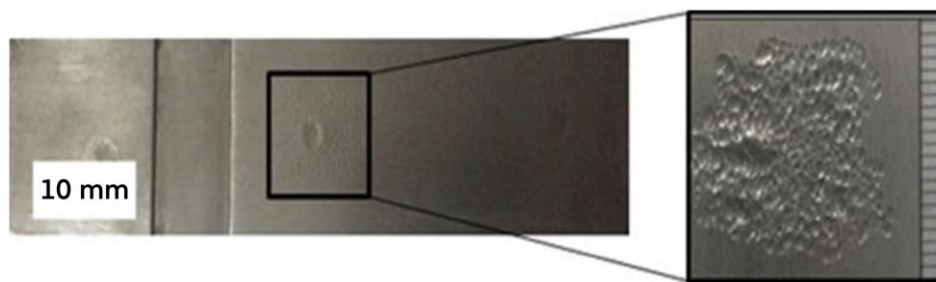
Aplicação de um PWIT (“*Post Weld Impact Treatment*”) no ponto de soldadura. Adaptado de [4]
